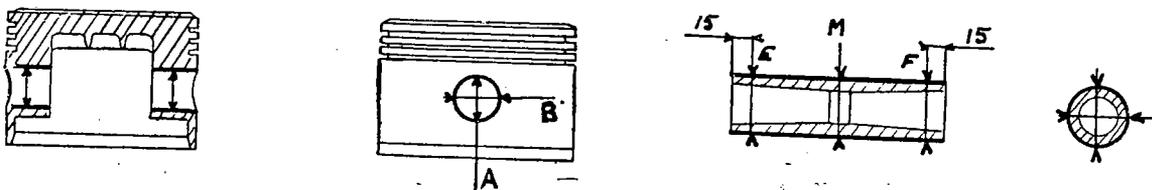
MESURATIONS DES PISTONS ET AXES DE PISTON
